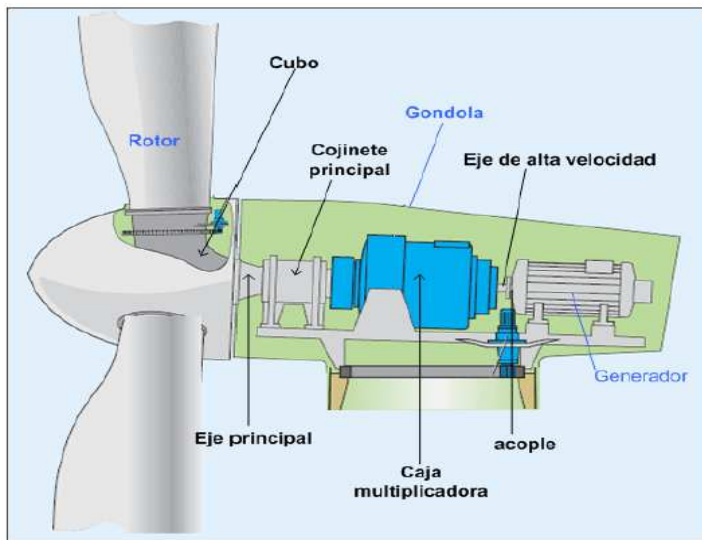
Elementos constitutivos del acoplamiento mecánico [10]
